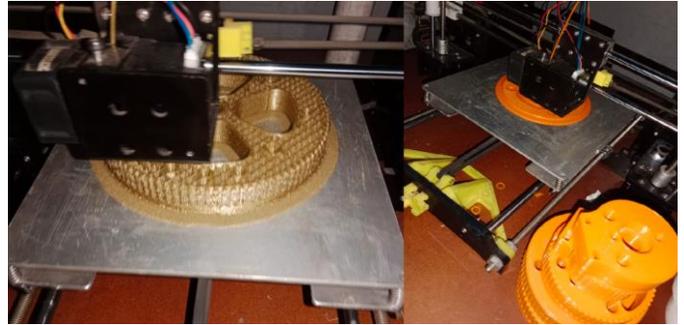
Impresión de piezas impresas en 3D, Fuente: Autor
